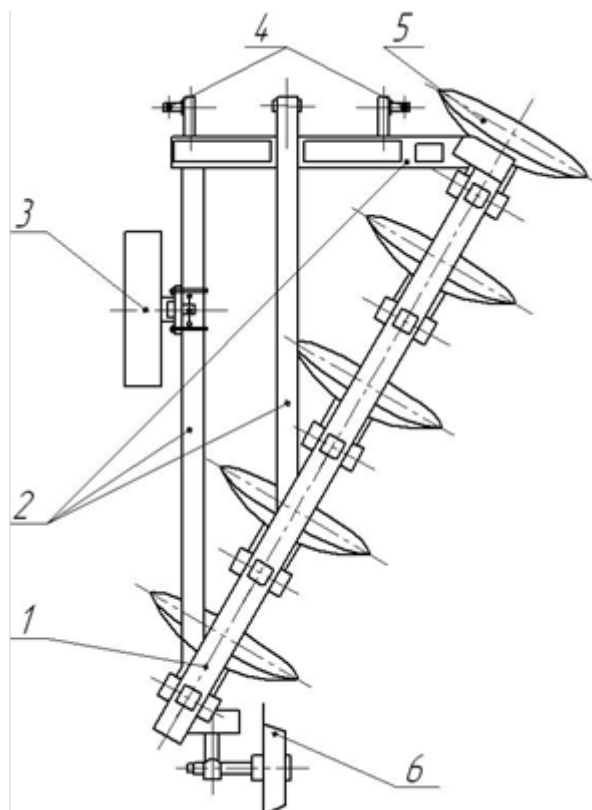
Схема дискового плуга: 1 – балка основна; 2 – рама; 3 – колес опорне; 4 – корпус дисковий; 5 – борозне колесо
